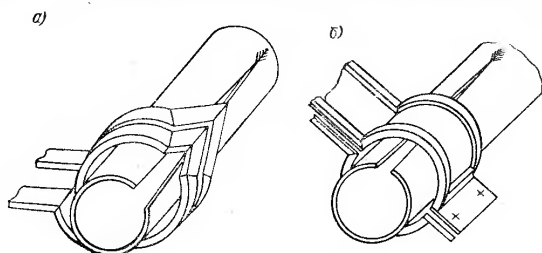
Охватывающие цилиндрические индукторы: а — с клином; б — съемный
